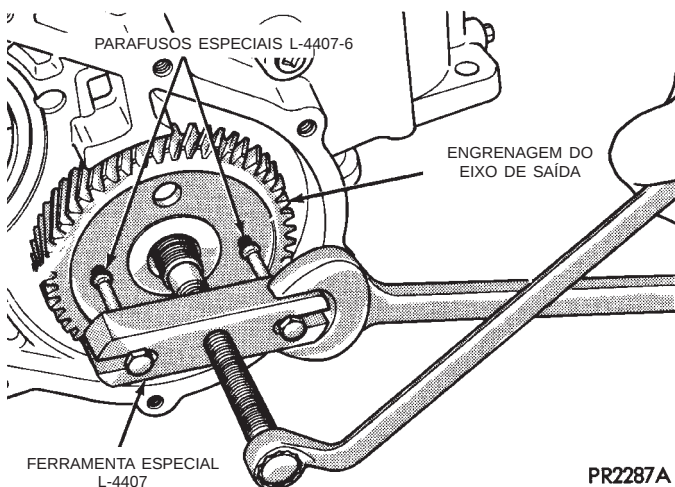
Remoção da Engrenagem do Eixo de Saída
